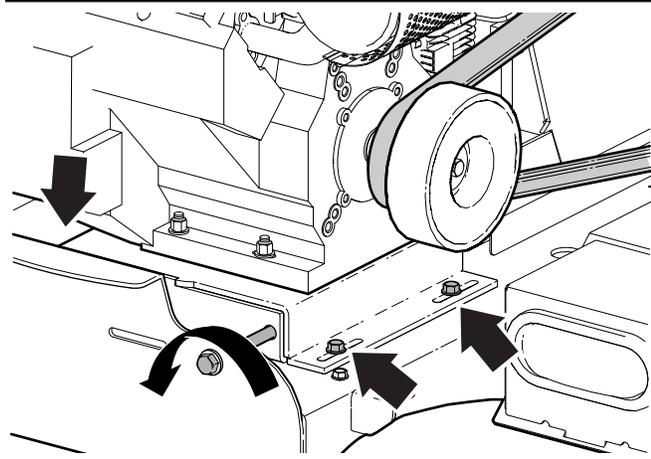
Boulon de réglage de la tension de la courroie d'entraînement
